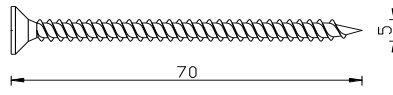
Deneylerde kullanılan kavela boyutları ve ölçüleri (mm)
